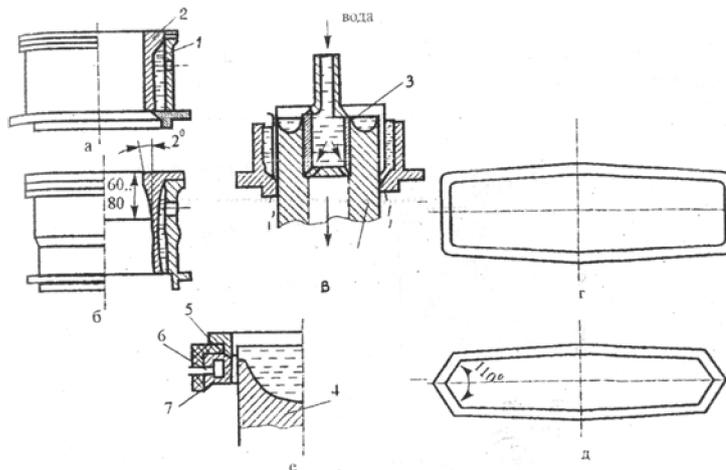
Схемы кристаллизаторов: а, б - для отливок сплошных слитков; в - полых цилиндрических слитков; г, д - для отливки плоских слитков; е - электромагнитный кристаллизатор; 1 - корпус, 2 - гильза, 3 - водоохлаждаемый стержень, 4 - слиток; 5 - экран, 6 - корпус, 7 - индуктор
